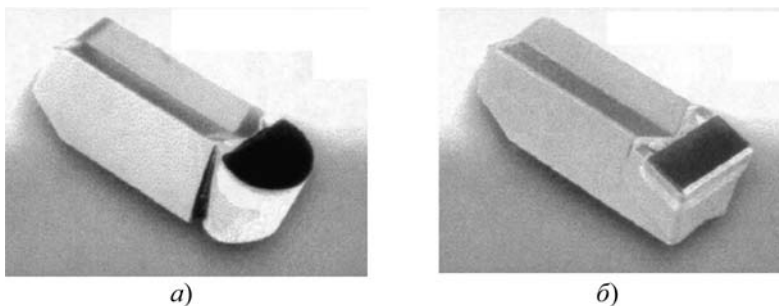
Паяные вставки из ПСТМ с круглым (а) и прямоугольным режущими элементами (б) для резцов системы Cut-Grip
